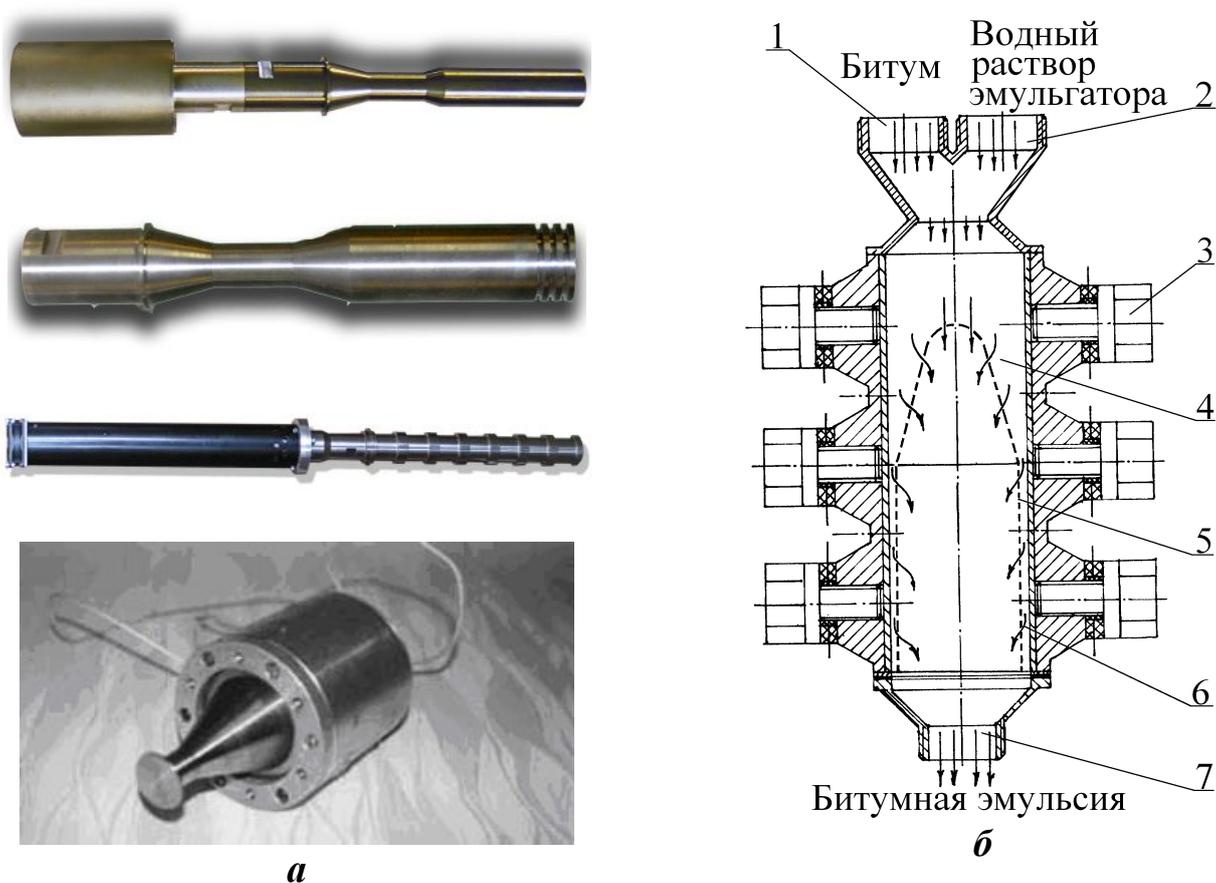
Внешний вид и схематическое изображение ёмкостных (а) и проточных (б) акустических диспергаторов: 1 – патрубок ввода битума; 2 – патрубок ввода водного раствора эмульгатора и кислоты или щёлочи; 3 – ультразвуковой вибратор; 4 – рабочая камера; 5 – фильтр с заданным размером ячеек для пропуска диспергированных частиц битума; 6 – движение диспергированных частиц битума через фильтр; 7 – выходной патрубок для эмульсии.
